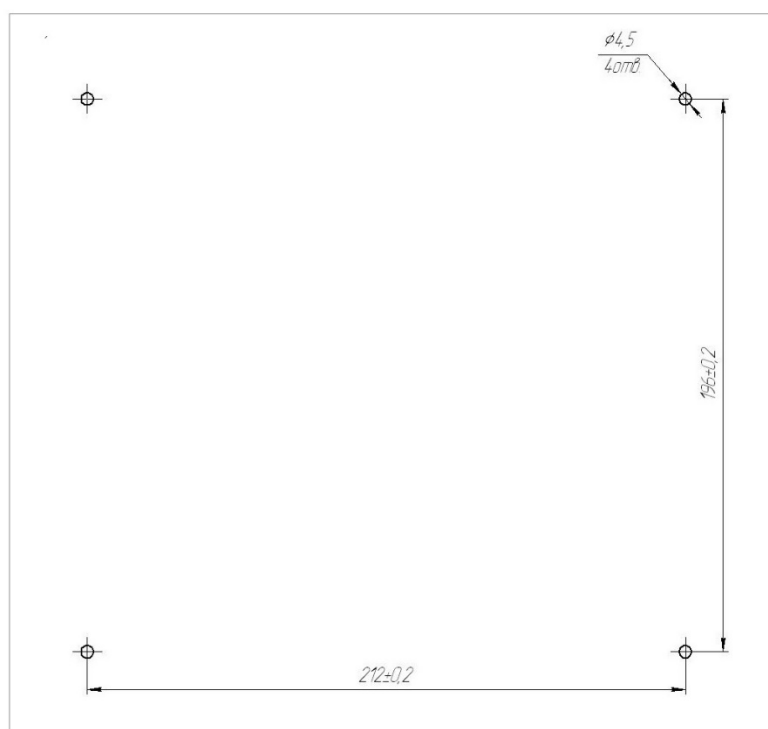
Габаритные размеры устройства РЗЛ-05МХ - В на виде сверху
